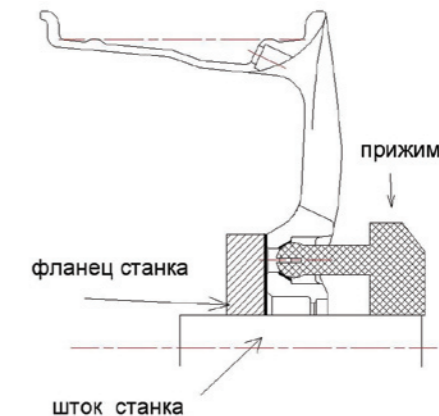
Закрепление колеса по привалочной плоскости и крепежным отверстиям (очень редкий случай)
